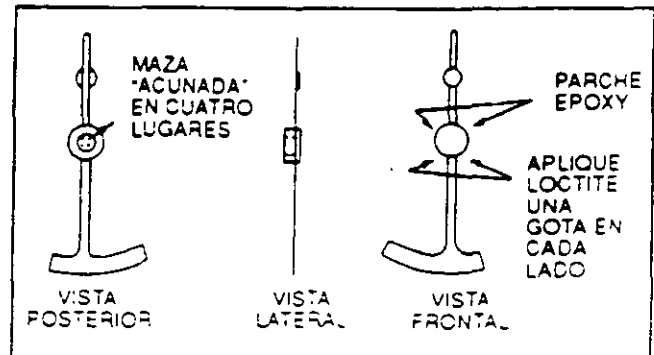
CONJUNTO DEL MANECILLAS E-24301-S
